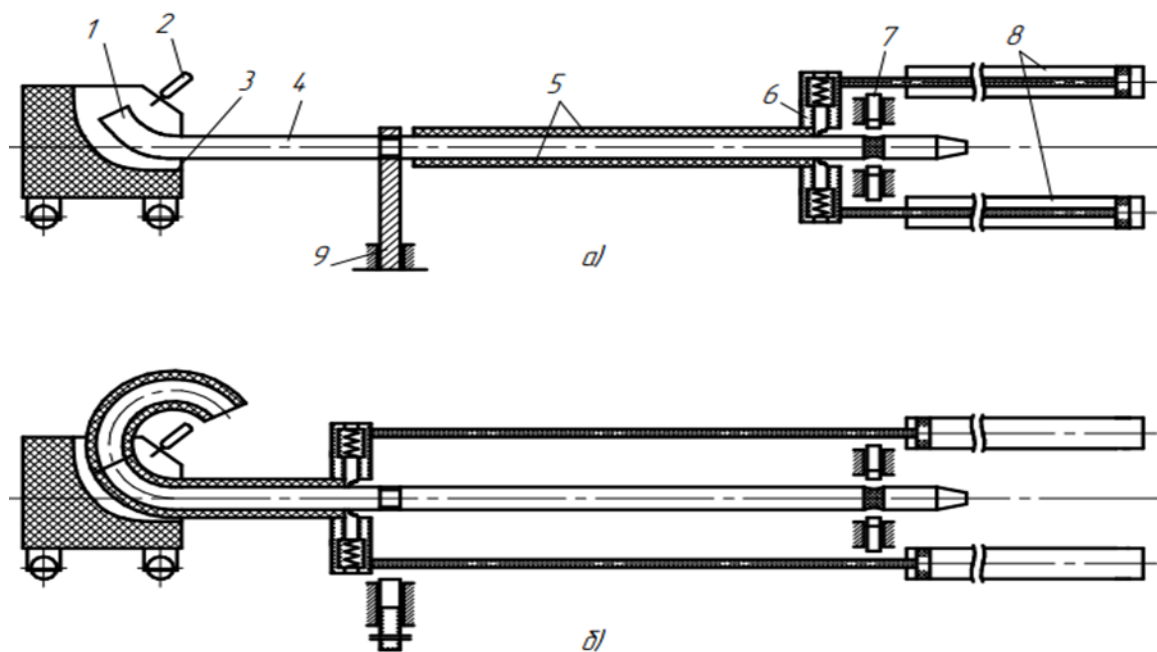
Схема процесса изготовления отводов горячей протяжки по сердечнику:
